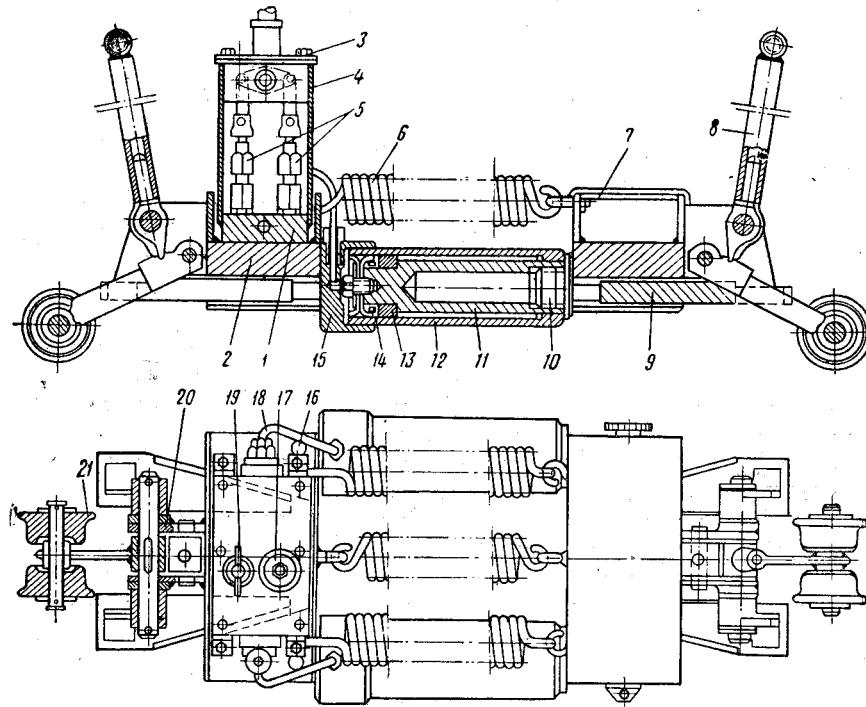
Гидравлический разгонщик стыковых зазоров конструкции Непомнящего (тип РН-01):
